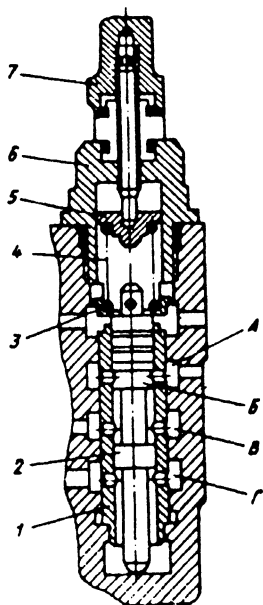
Блокировочный золотник исполнительного механизма:
